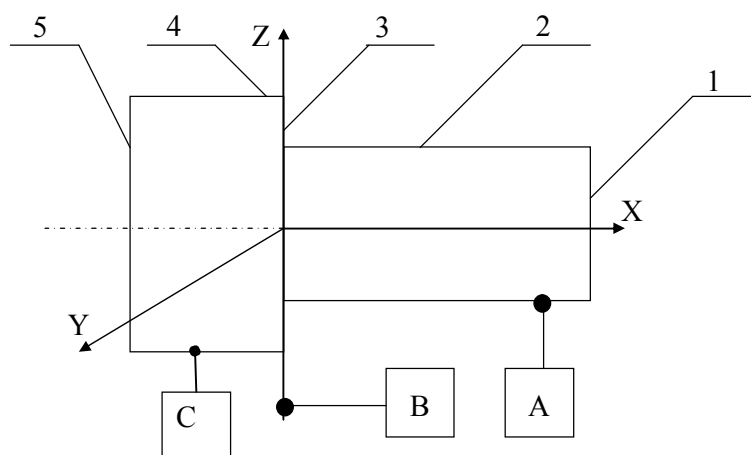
Деталь типу «багатоступінчатий вал»
